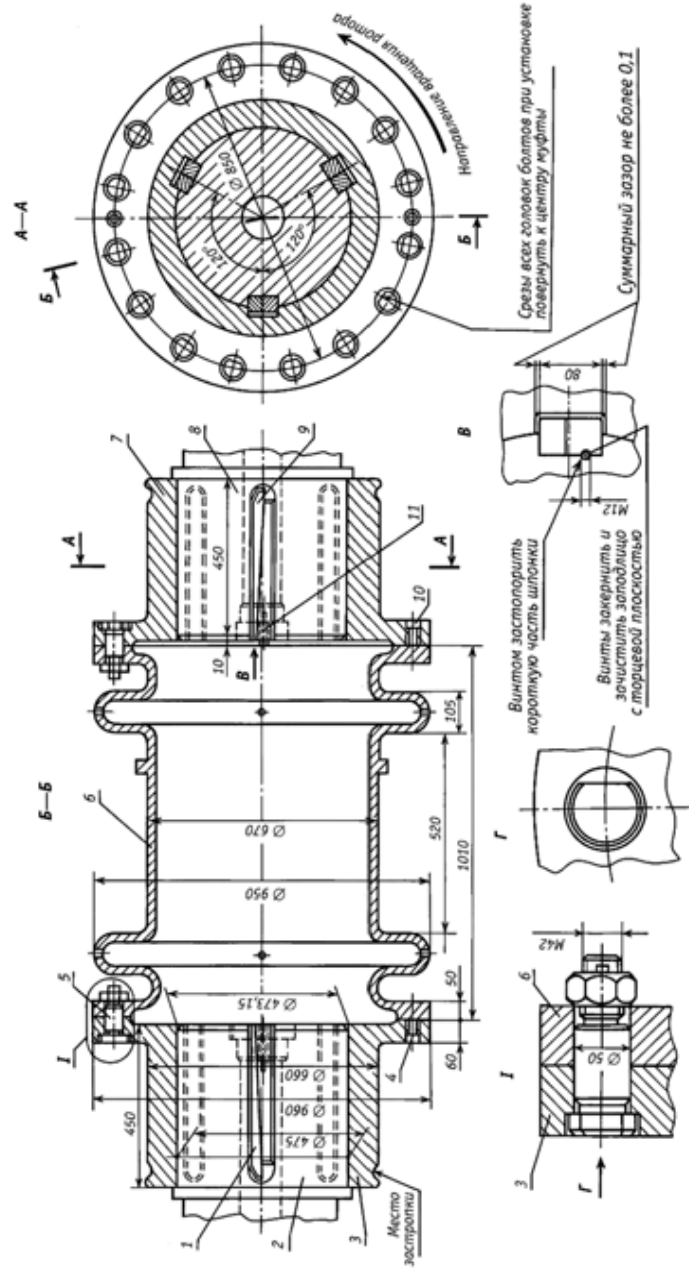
Полужесткая муфта ЛМЗ: 1, 9 – клиновидная шпонка; 2 – вал ротора ЦСД; 3 – полумуфта на валу ротора ЦСД; 4, 10 – отверстия для отжимных болтов; 5 – призонные болты; 6 – соединительный элемент; 7 – полумуфта ротора ЦНД; 8 – вал ротора ЦНД; 11 – винт
